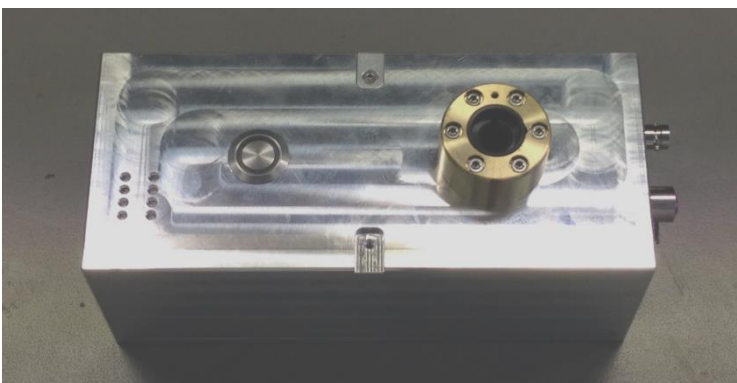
Gehäuse (Corrado Zeichnungs-Nr.: 3xxxxxxx)
